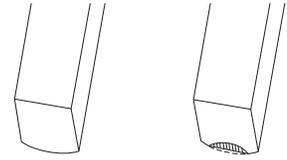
Résultat d'un affûtage sur une pierre creuse et d'une finition sur une pierre plane
